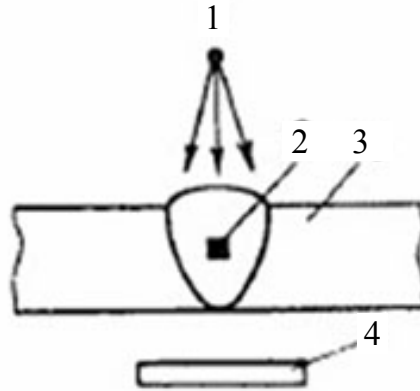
Схема просвечивания сварного соединения:
